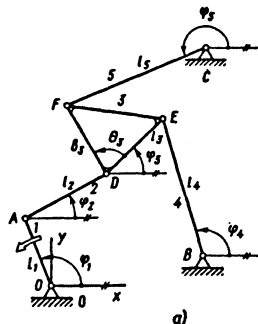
Шестизвенный плоский шарнирный механизм с трехзвеновой группой:
